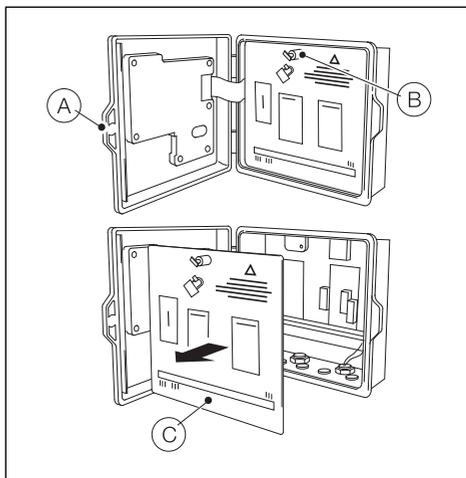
Acceso a la tarjeta de conexión del controlador CMF310
